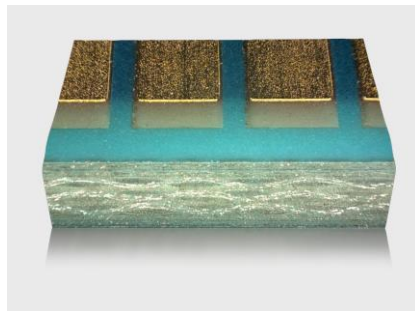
Mikroskop-Aufnahme einer Schnittkante: Glatte Oberfläche, schneller Schnitt. Mit PicoLine-Systemen lassen sich die gängigen Leiterplattenmaterialien in kürzester Zeit sauber und rückstandsfrei bearbeiten.
